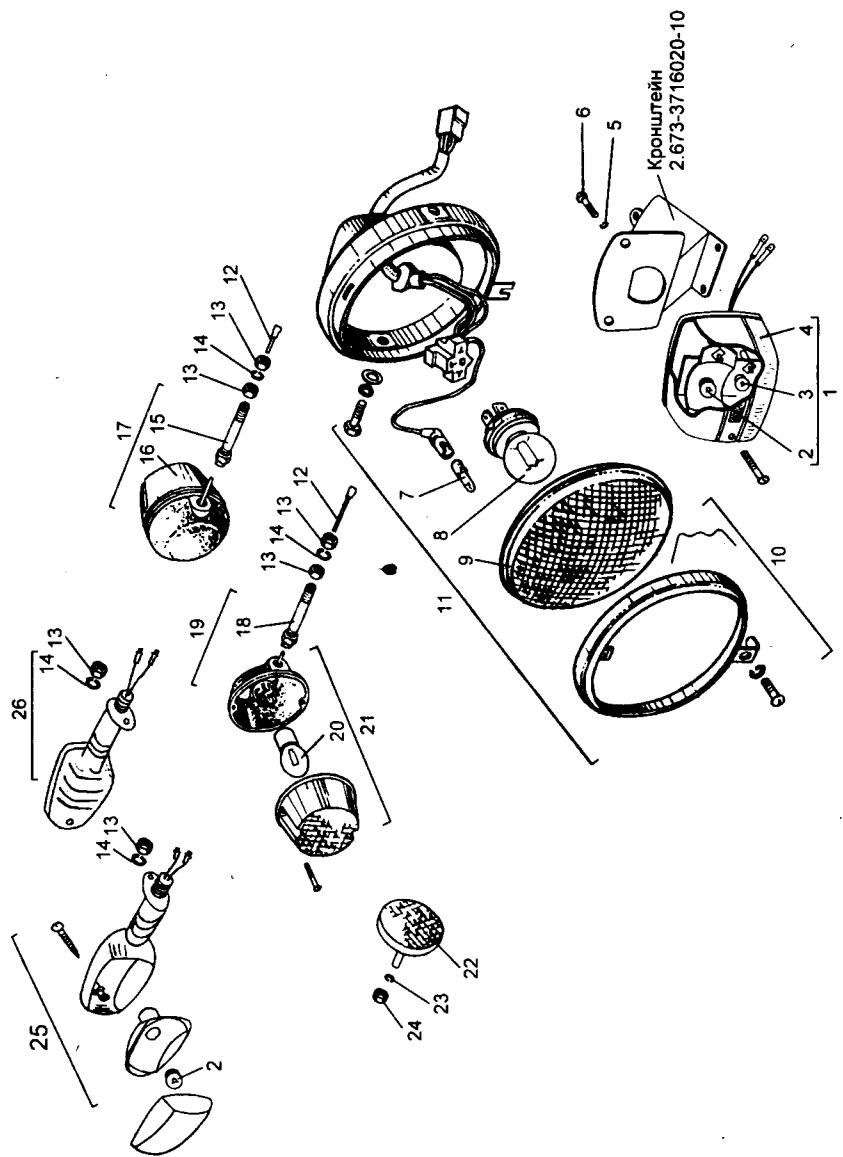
Фара, указатели поворота, задний фонарь, световозвращатели
